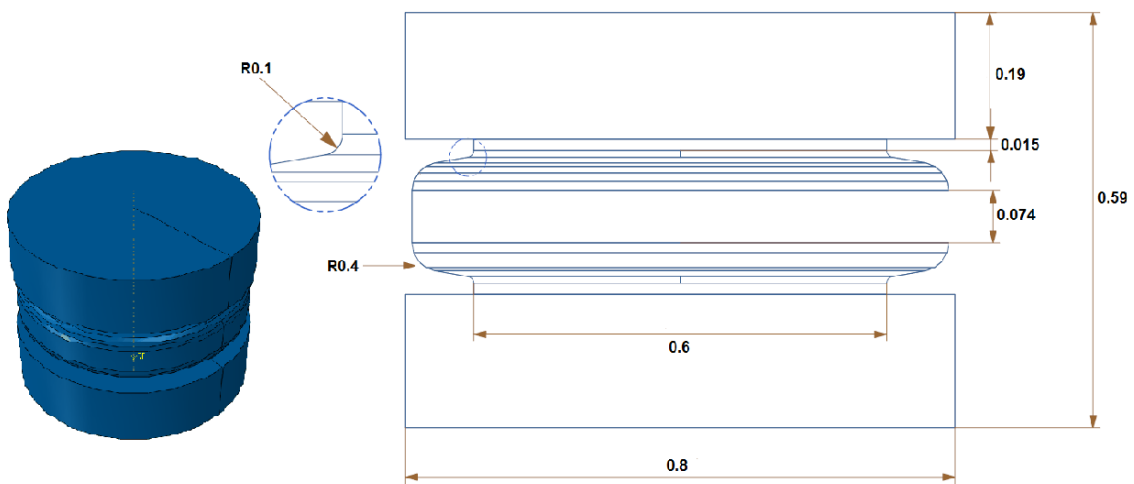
Geometría del rodillo 2, dimensiones en [m].
